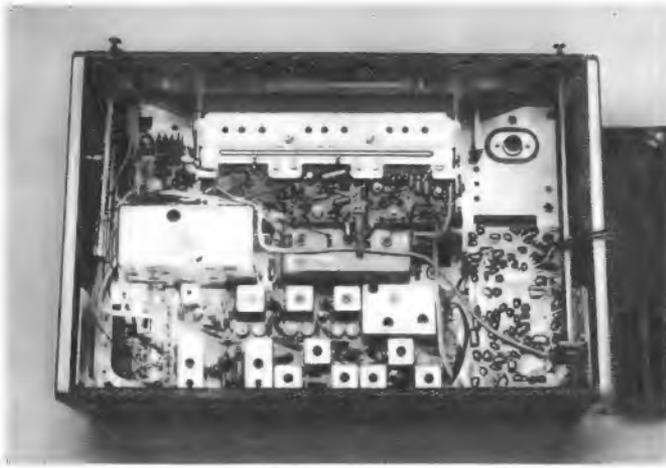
Das aus Baugruppen zusammengesetzte Chassis. Oben die sehr lange Ferritstabantenne
